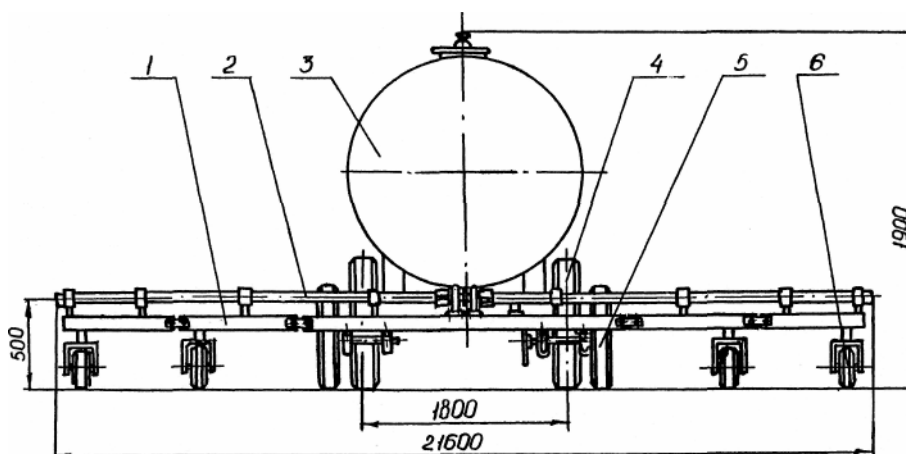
Общий вид агрегата для внесения ТО шириной захвата 21,6 м (вид сзади):
